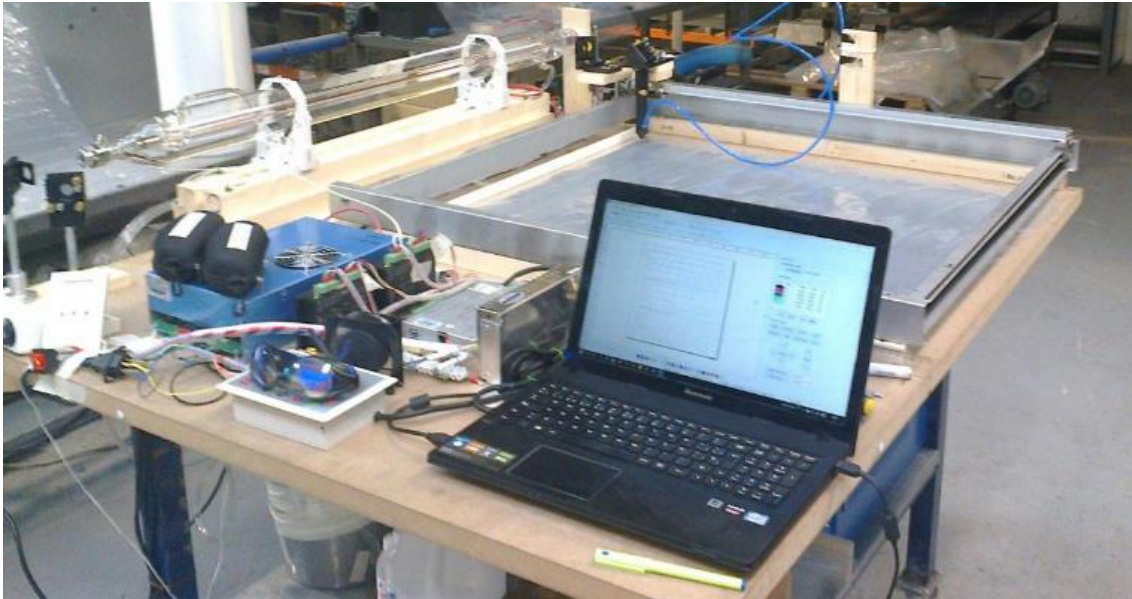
Sistema de mesa x-y para soldadura por láser
